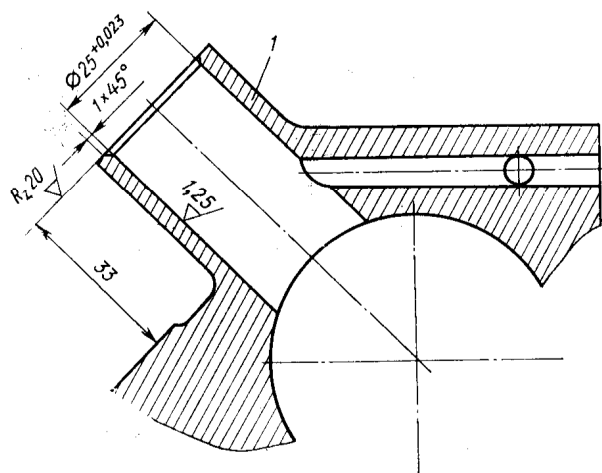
Расточка картера двигателя под ремонтные втулки бонков толкателя:
